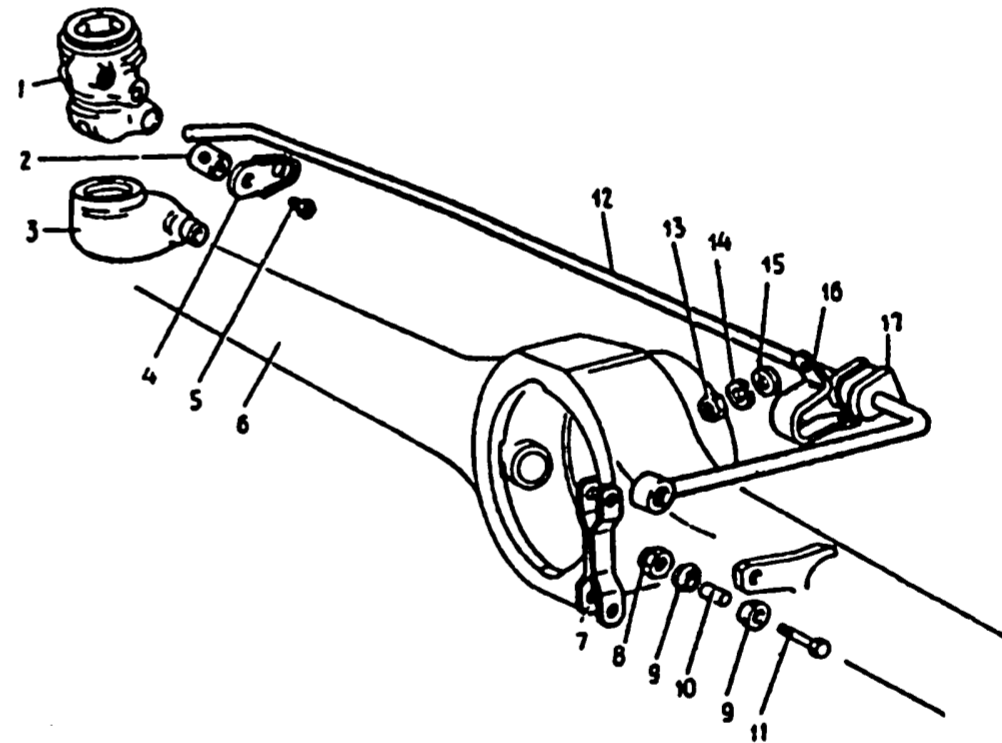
Детали привода регулятора давления: 1 - регулятор давления; 2 - ось рычага привода регулятора давления; 3 - грязезащитный колпачок; 4 - стопорная пластина; 5 - болт с пружинной шайбой; 6 - задний мост; 7 - тяга соединения рычага привода регулятора давления с кронштейном заднего моста; 8 - гайка болта; 9 - пластмассовая втулка; 10 - распорная втулка; 11 - болт крепления тяги; 12 - рычаг привода регулятора давления; 13 - гайка для крепления скобы к кузову; 14 - пружинная шайба; 15 - плоская шайба; 16 - скоба крепления рычага привода регулятора давления; 17 - резиновая втулка
